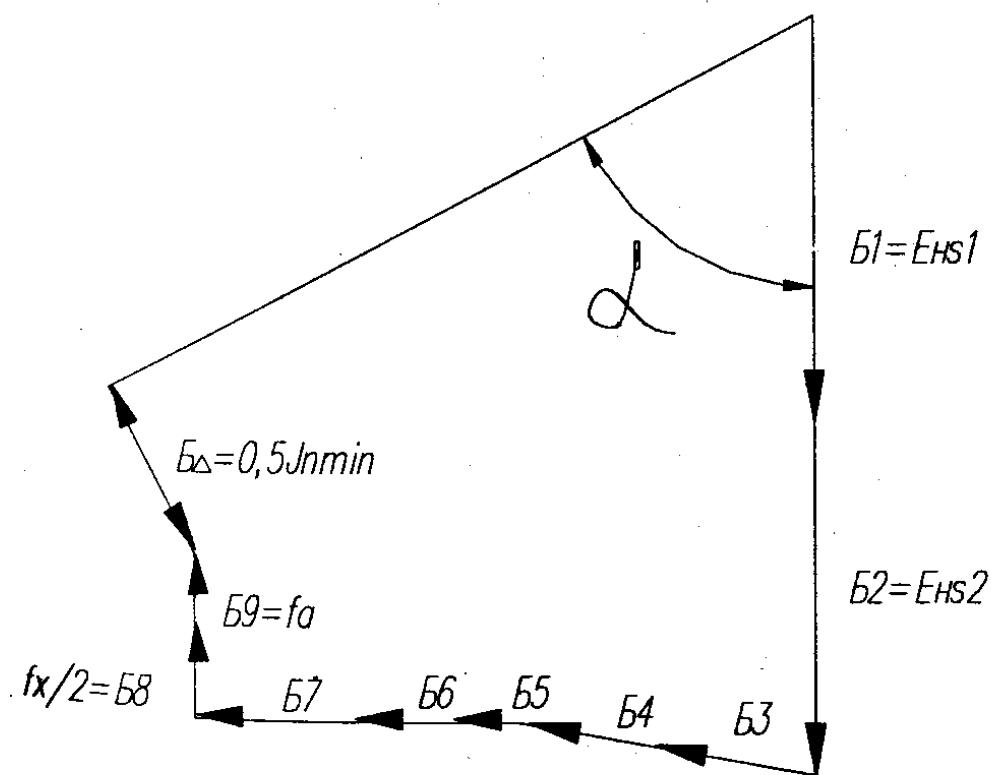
Размерная цепь для половины бокового зазора цилиндрической зубчатой передачи
